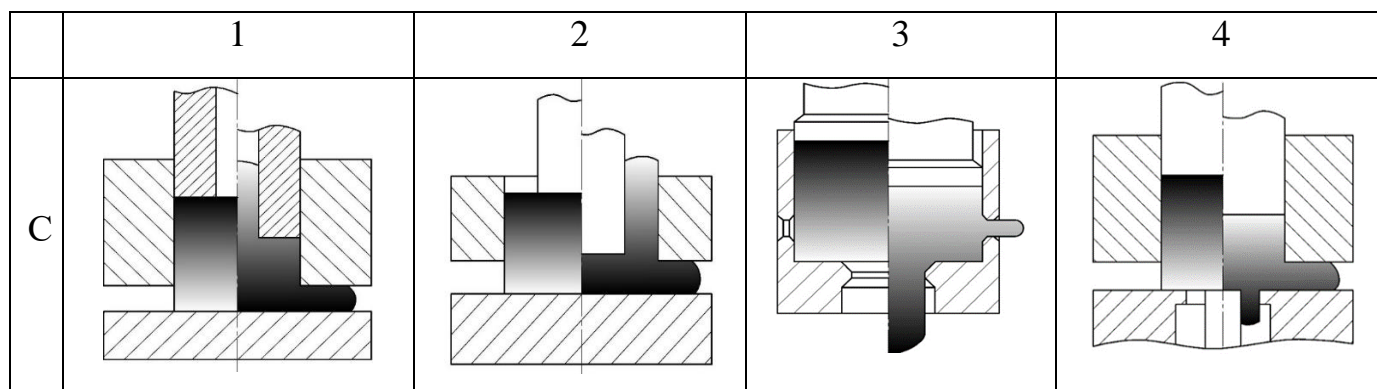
Схеми комбінованого радіально-поздовжнього видавлювання з двома степенями свободи течії металу
